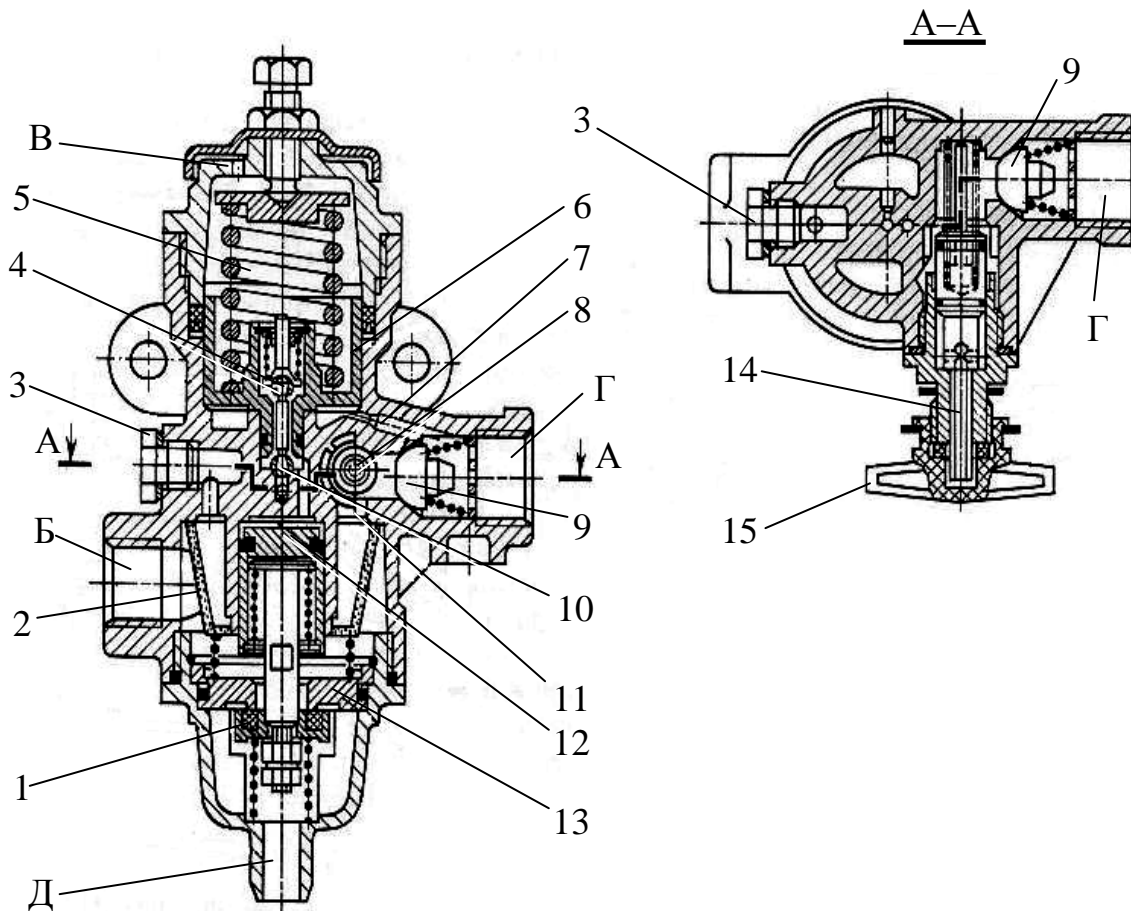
Регулятор давления тормозного привода грузового автомобиля-тягача КАМАЗ-5320: 1 – разгрузочный клапан; 2 – фильтр; 3 – пробка; 4 – выпускной клапан; 5 – уравнивающая пружина; 6 – следящий поршень; 7 и 11 – каналы; 8 – кольцевой канал; 9 – обратный клапан; 10 – впускной клапан; 12 – разгрузочный поршень; 13 – седло клапана 1; 14 – клапан для отбора воздуха при накачивании шин; 15 – колпачок; Б – вывод для подключения компрессора; В и Д – выходы в атмосферу; Г – вывод в пневмосистему
